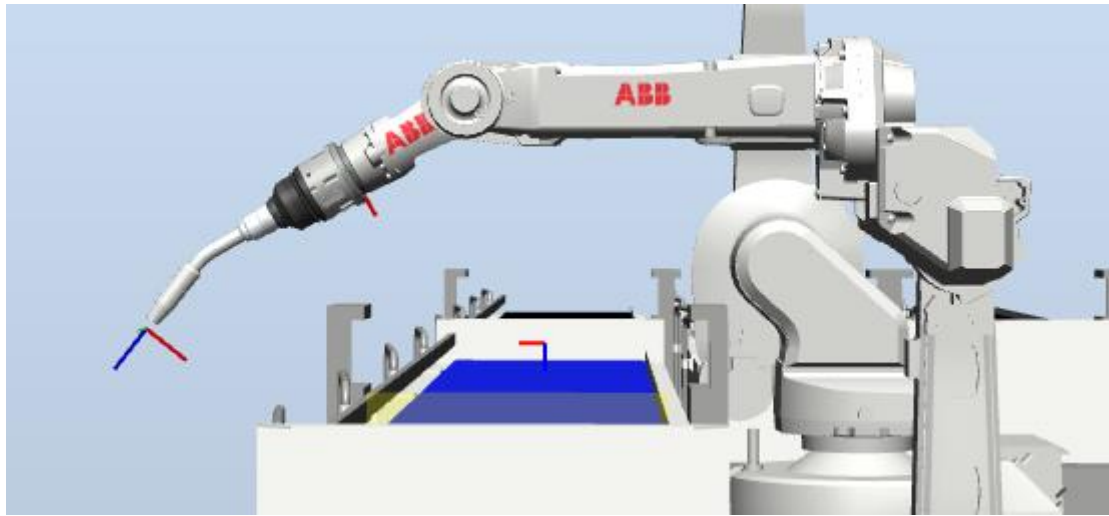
Conexión herramienta de soldar con IRB 1520ID
